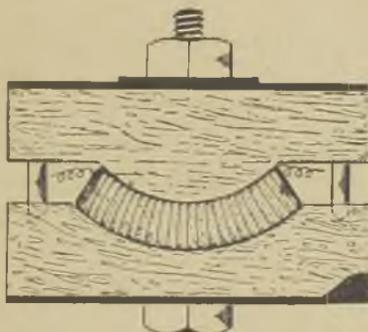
Holzschablone zum Biegen von Feldspulen.
